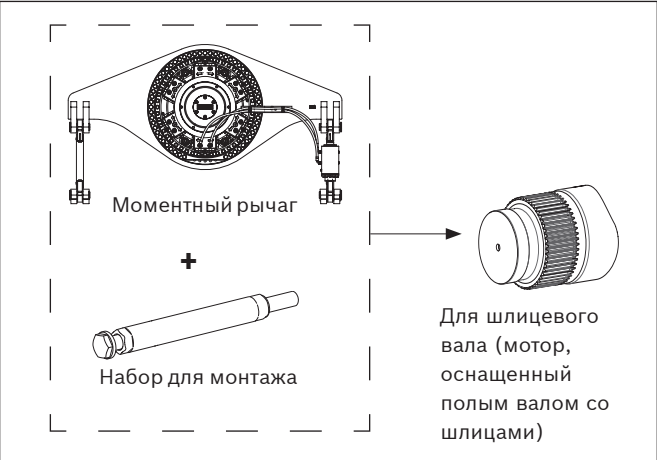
Установка с использованием моментного рычага с двумя плечами на шлицевом валу
